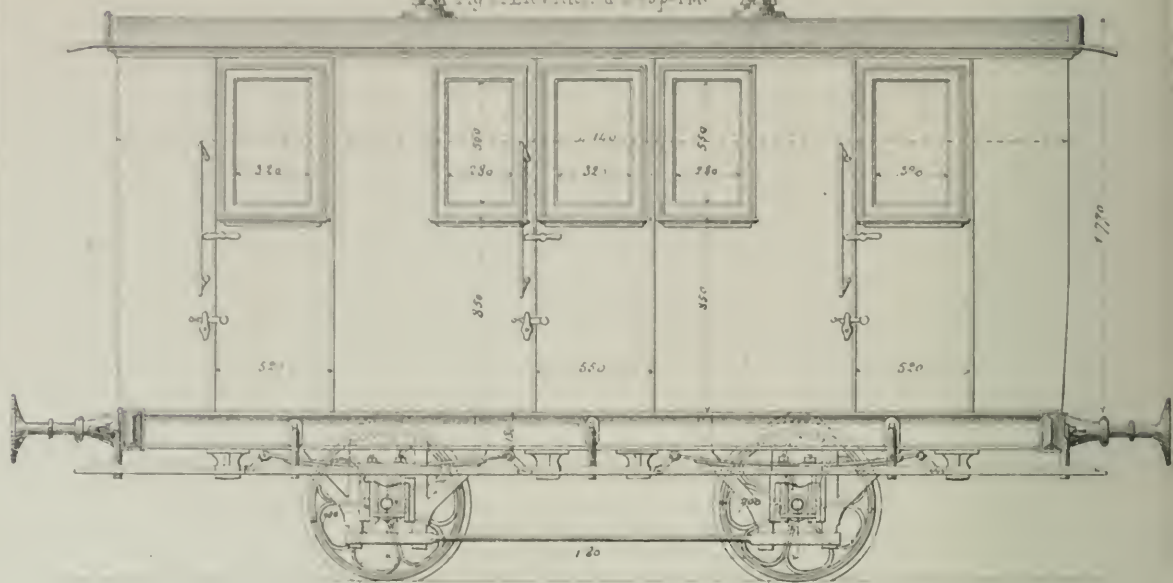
Dessin plan, Châssis et Coupe de la Caisse à 0°03 pour 1 M.
